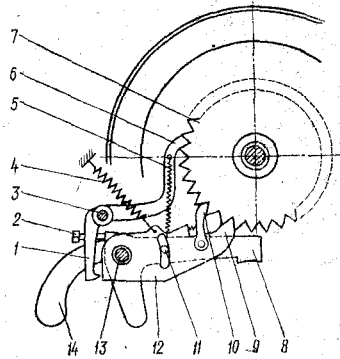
Схема механизма поворота батареи станка АТ-100-5М
